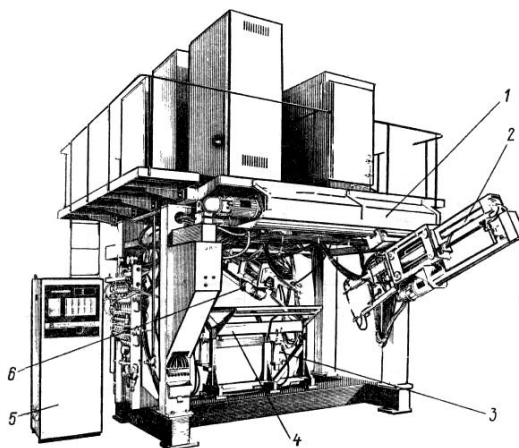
Многоэлектродная контактная сварочная машина на базе портального четырёхстоечного прессы
